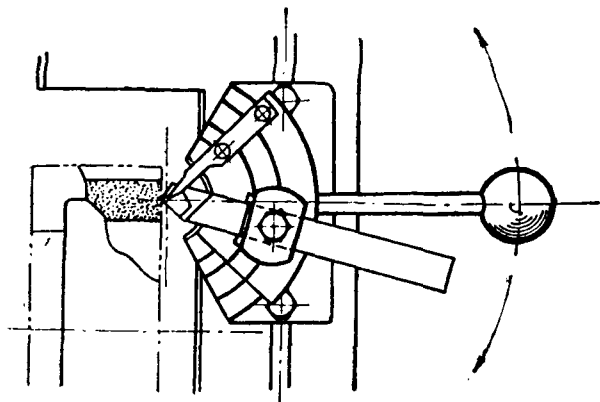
Приспособление для заточки радиуса при вершине реза. Рабочее движение
